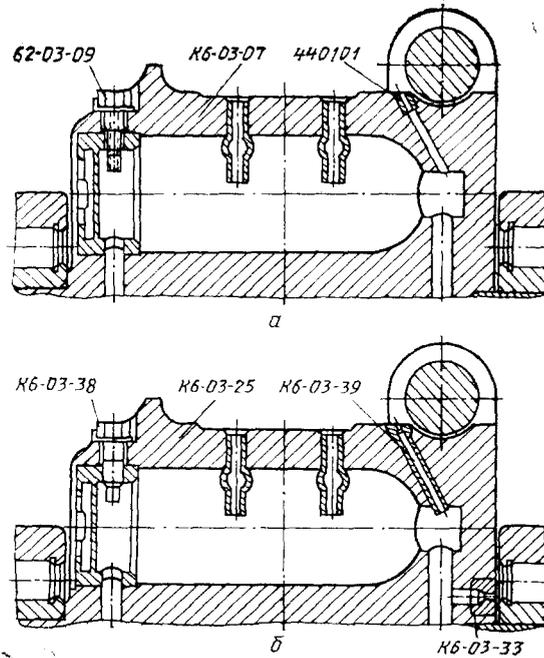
а. Калиброванные отверстия и жиклеры в щеках коленчатого вала двигателя, предназначенные для смазки цилиндрно-поршневой группы (ТК № 5, вып. 25): А — на двигателях до 17 сер., Б — на двигателях 17 сер.
